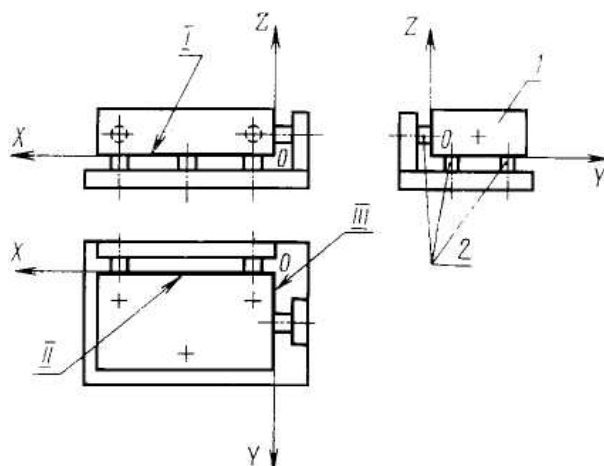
Установочная, направляющая и опорная базы заготовки:
